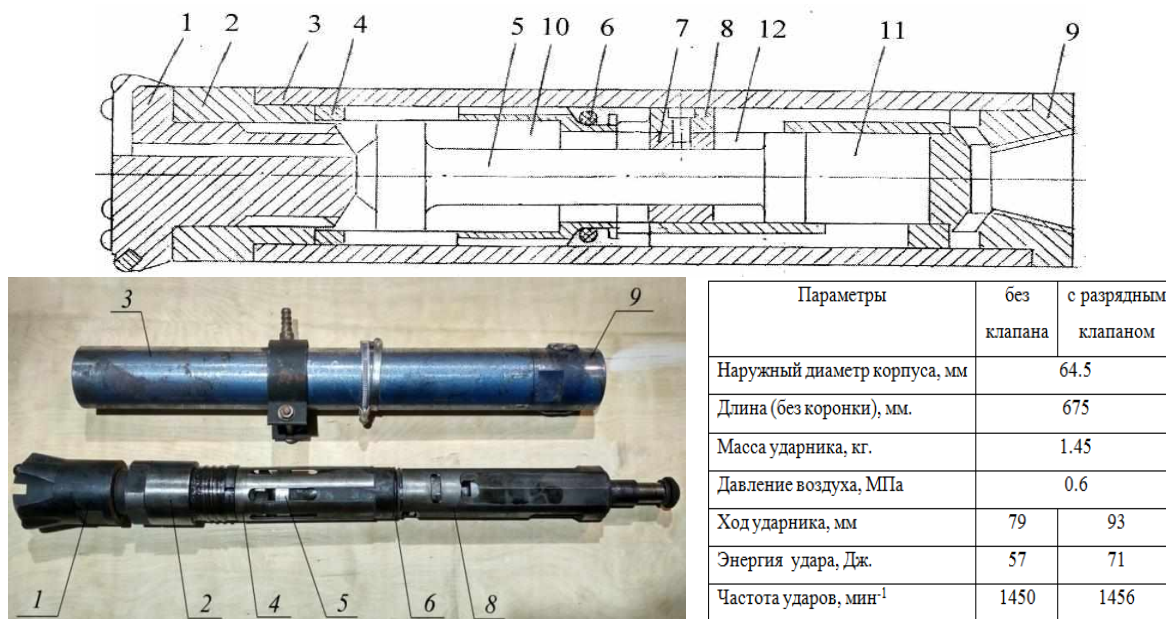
Принципиальная схема погружного пневмоударника с режимом разрядки рабочих камер: 1 – буровая коронка; 2 – букса; 3 – корпус; 4 – гильза передняя; 5 – ударник; 6 – эластичный клапан; 7 – кольцо разрезное; 8 – гильза задняя; 9 – переходник; 10 – кольцевая камера рабочего хода; 11 – торцевая камера рабочего хода; 12 – камера холостого хода постоянного давления
